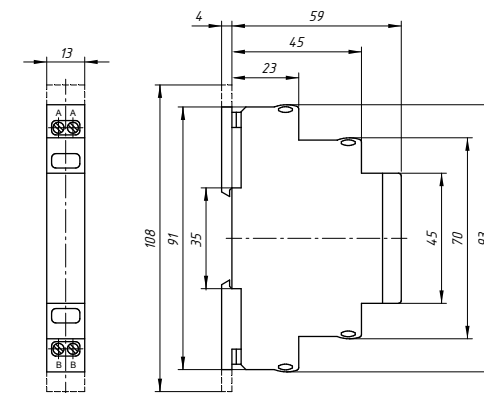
Габаритные и присоединительные размеры RC-модуля
